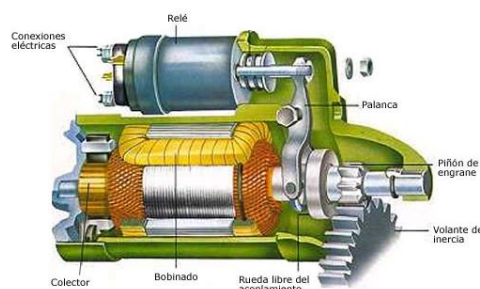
Imagen que muestra los componentes básicos de un motor de arranque
